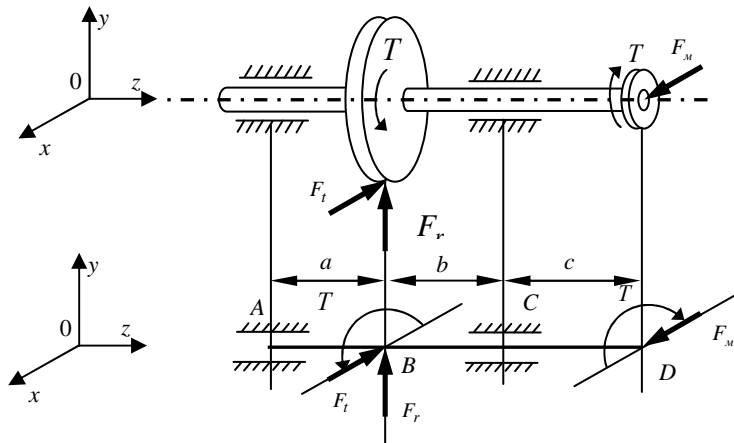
Переход от реальной конструкции к расчетной схеме
